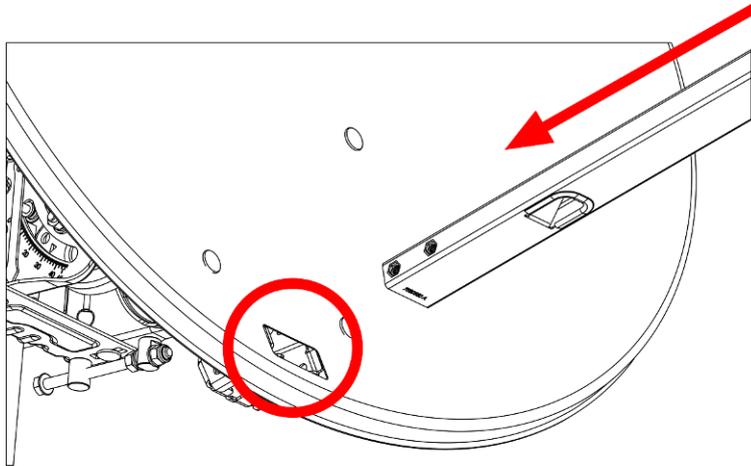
Вставка штанги облучателя в задний кронштейн
